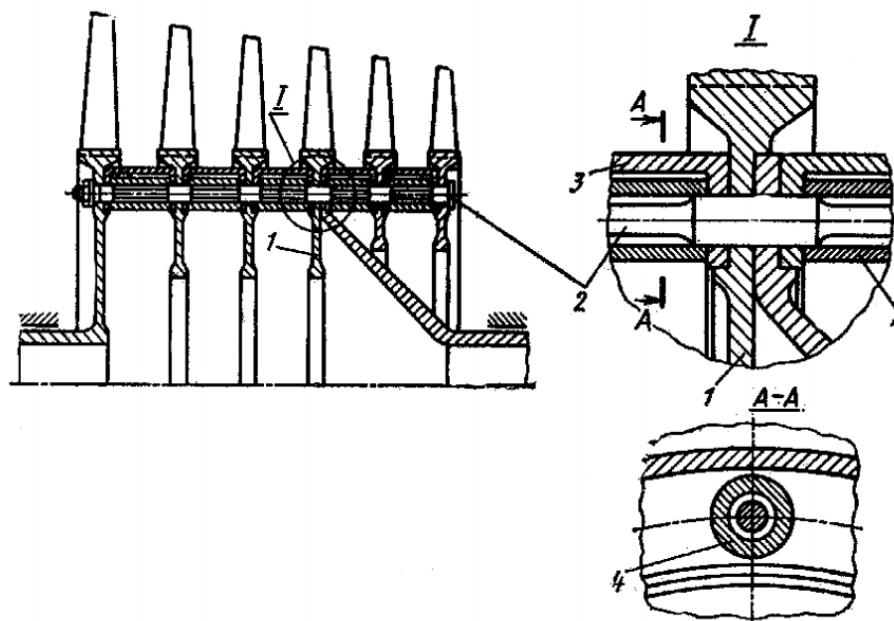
Ротор компрессора, в котором диски и проставки соединены длинными стяжными болтами и распорными втулками.
